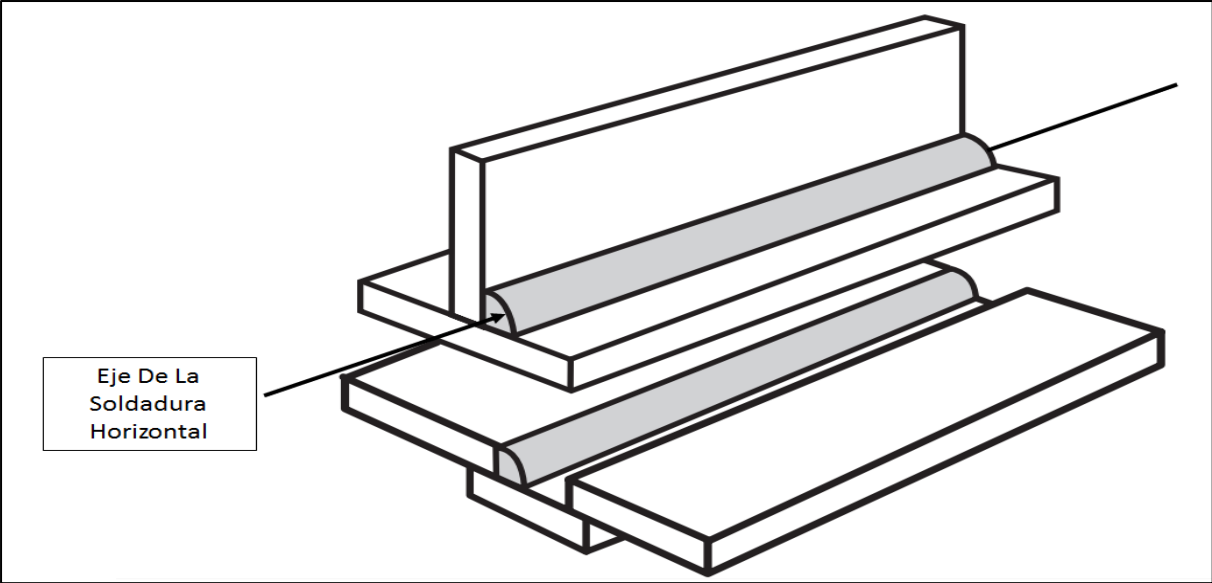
Soldadura De Filete En Posición 2F [58].
